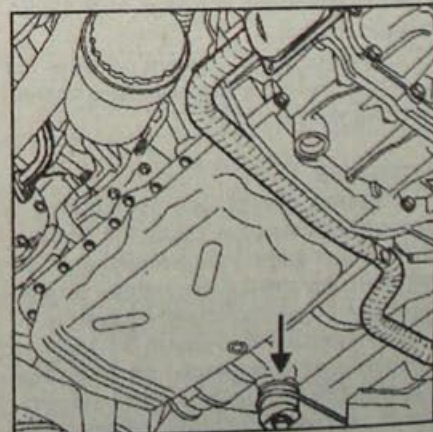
Расположение реактивной тяги крепления двигателя
